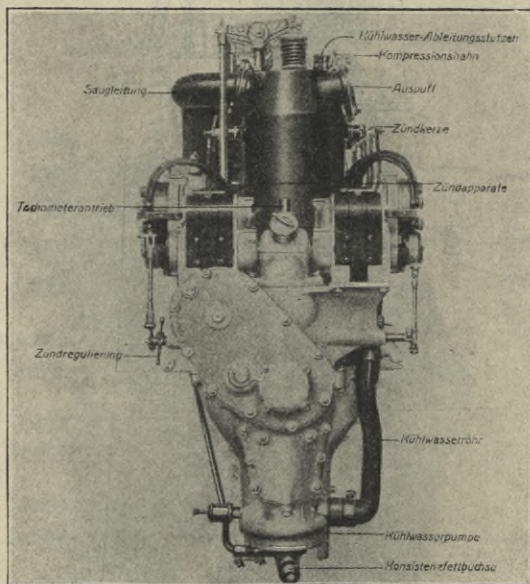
180 PS-Argus-Motor (Rückseite).
